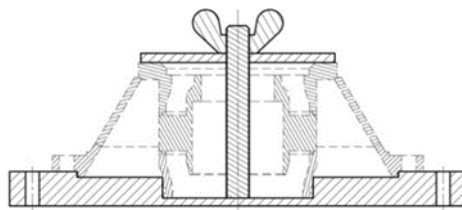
Эскиз сборочно-сварочного приспособления
